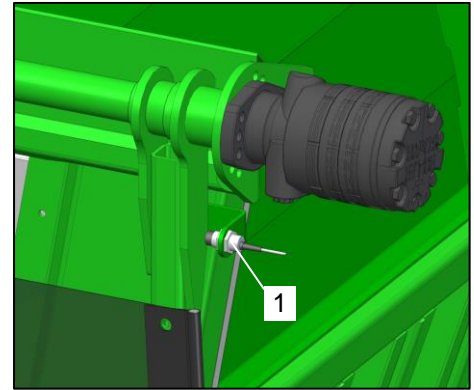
Capteur du recouvrement de l'espace de chargement à droite
